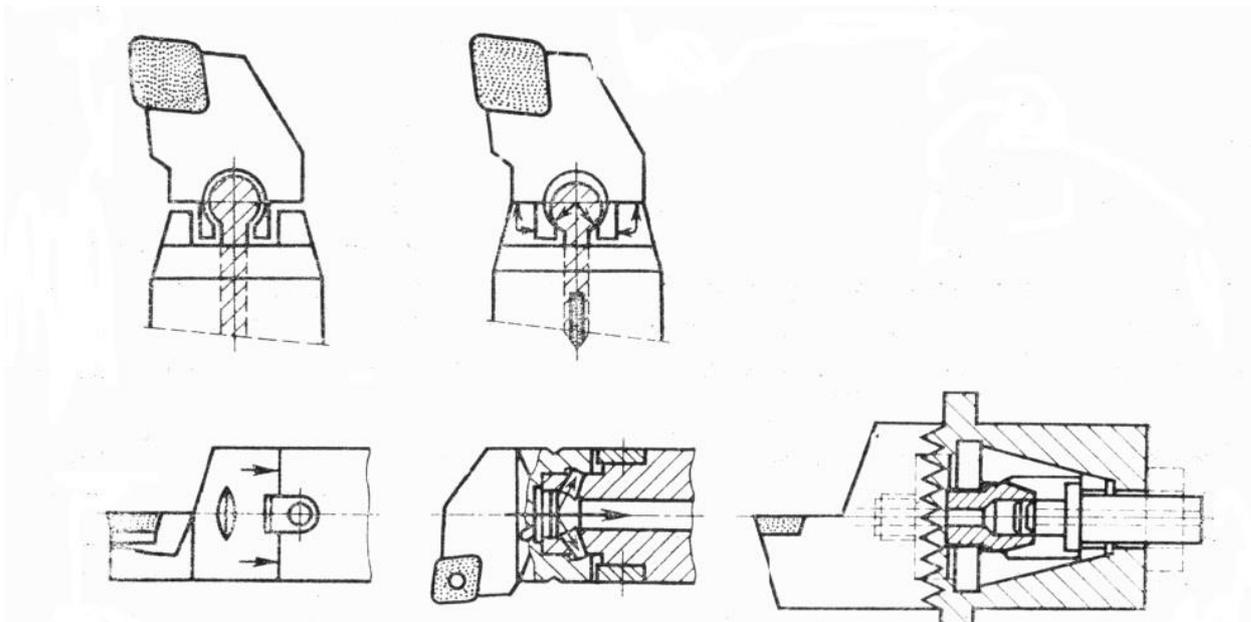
Конструкции резцов с механическим соединением режущих головок
